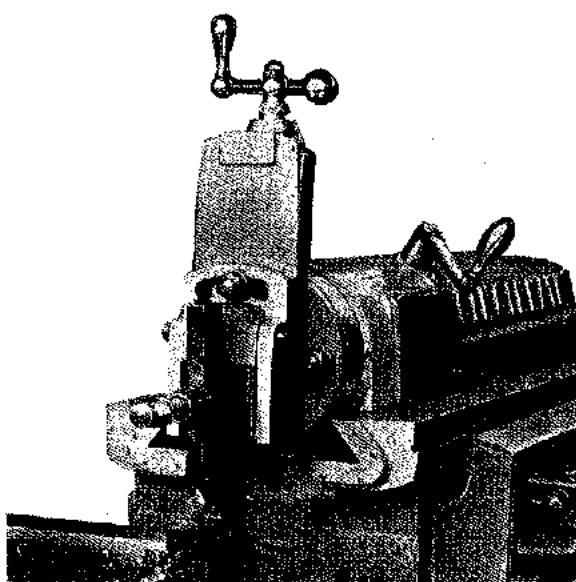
Cabezal de herramienta (Cincinnati Shaper Co.)
